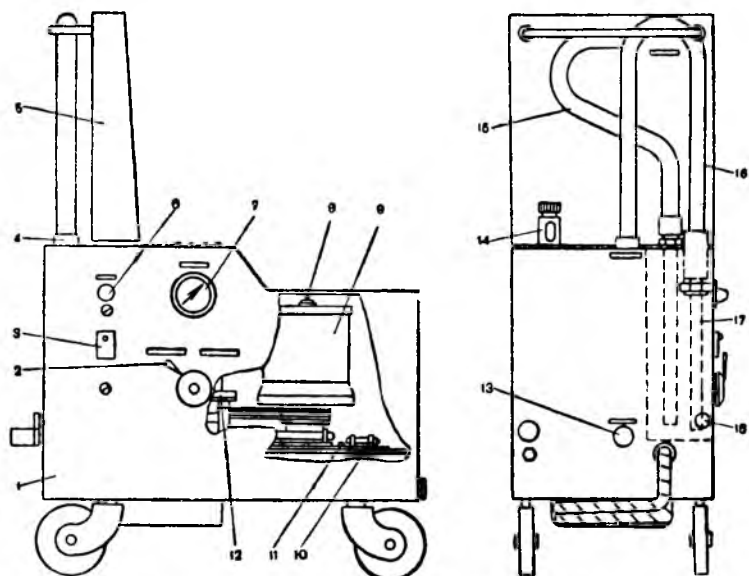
Малогабаритная центробежная установка УМЦ-901А:
